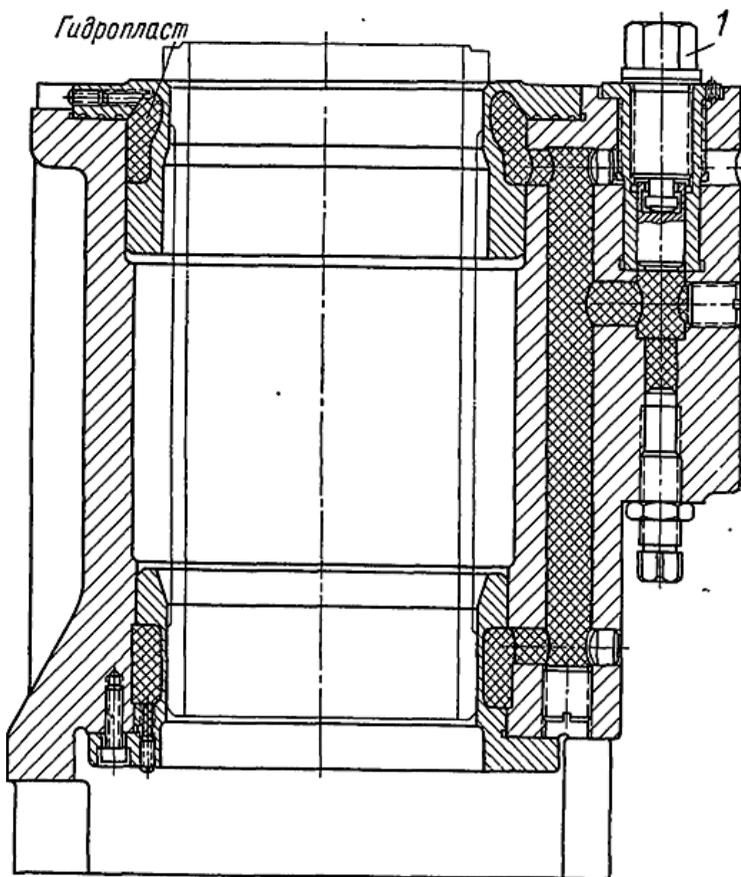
Приспособление с гидропластмассой для хонингования
